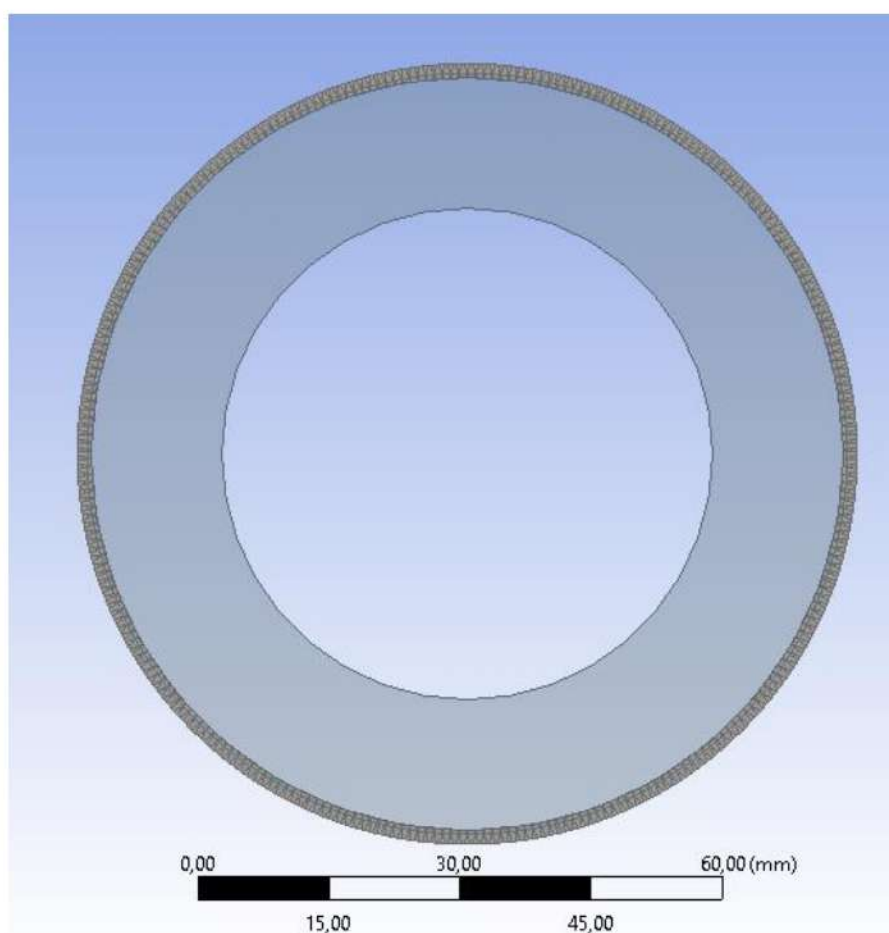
Геометрическая модель заготовки гибкого колеса на оправке
